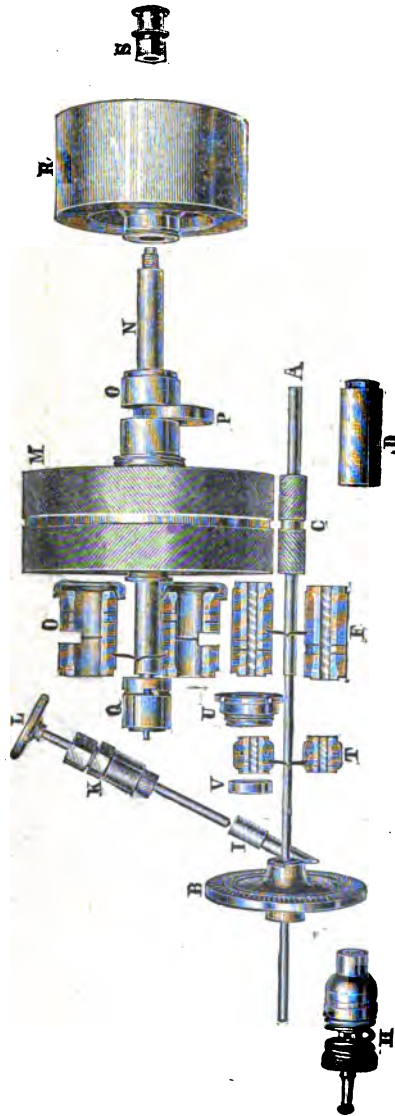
à 68. — Principaux organes de la turbine à vapeur de Laval. — A, arbre de la turbine. — B, roue à aubes. — C, pignon. — D, coussinet du bout d'arbre. — F, O, coussinets en deux pièces. — H, coussinet à rotule. — I, ajustage. — K, L, obturateur de l'ajutage. — M, roue dentée. — N, arbre moteur. — P, anneau graisseur. — Q, régulateur. — R, Poulie. — S, contre-écrou. — T, obturateur de vido.
